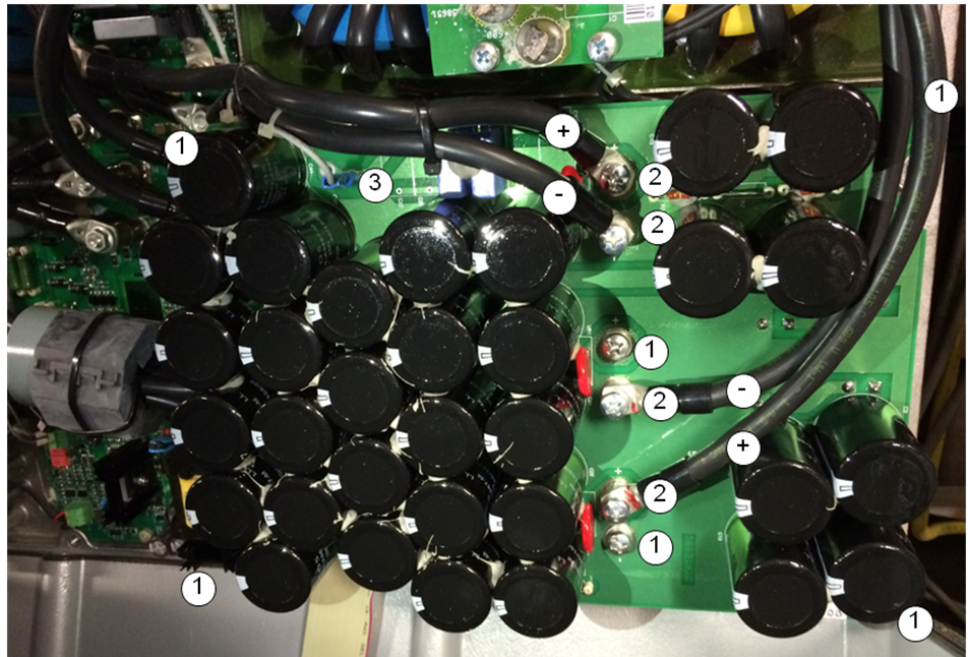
Befestigung des werkseitigen eingebauten Kondensatormodul
